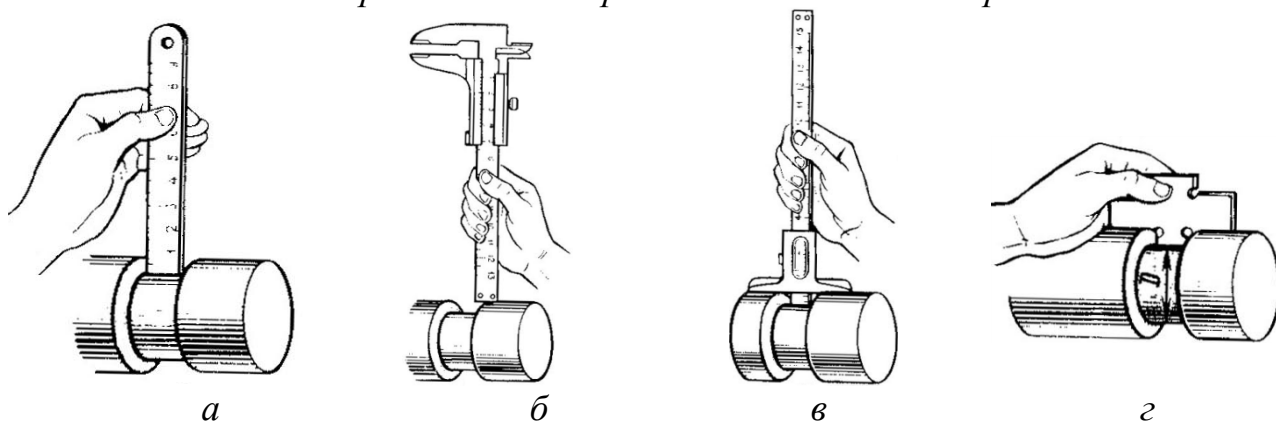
Схема измерения глубины канавки: *а* — линейкой;
